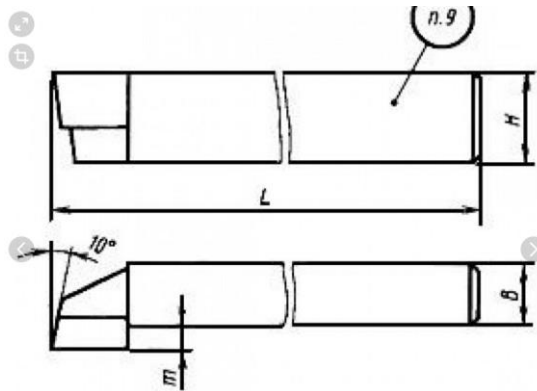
Резец проходной упорный 2101-0565 ГОСТ 18870-73.
